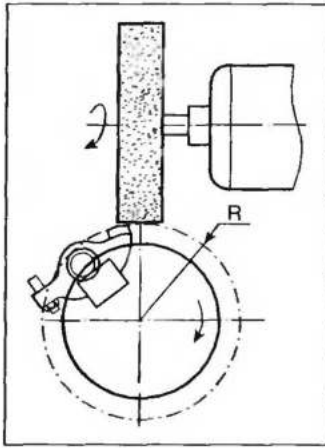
Схема шлифования коромысла на поворотном столе (R - радиус закругления опорной поверхности коромысла)
